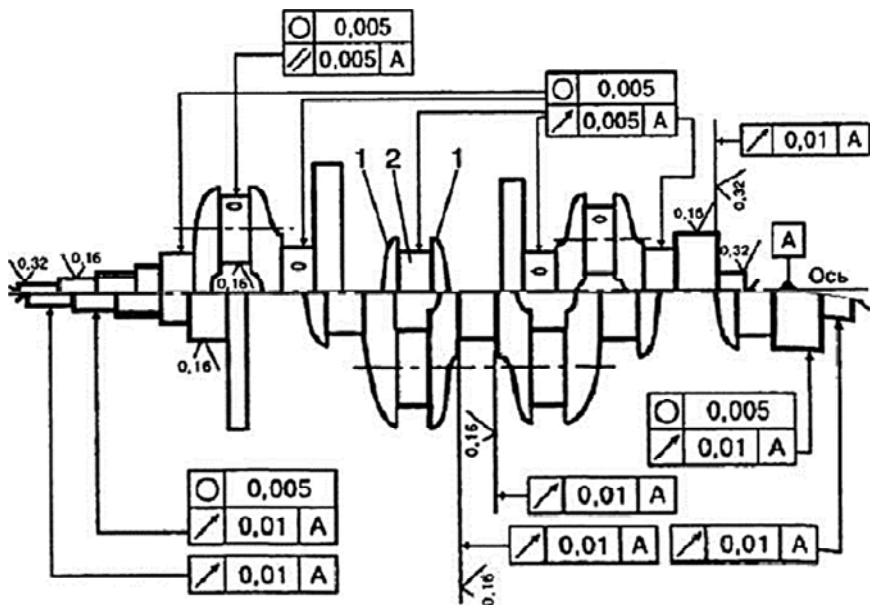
Схема и основные требования к качеству и расположению поверхностей коленчатого вала:
